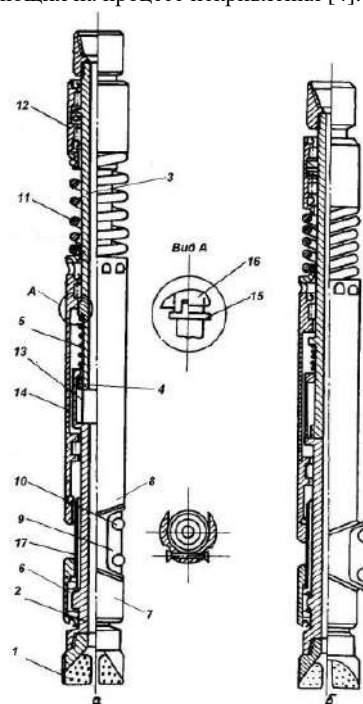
Общий вид отклонителя ТЗ-3: а – транспортное положение; б – рабочее положение; 1 – долото; 2 – нижний вал; 3 – верхний вал; 4, 13 – шлицевое соединение; 5 – роторная пружина; 6 – нижний подшипниковый узел; 7 – нижний полуклин; 8 – верхний полуклин; 9 – подвижной клин-ползун; 10 – каретка с катками; 11 – статорная пружина; 12 – верхний подшипниковый узел; 14 – корпус; 15 – блокировочный фиксатор; 16 – блокировочная муфта; 17 – трубка
